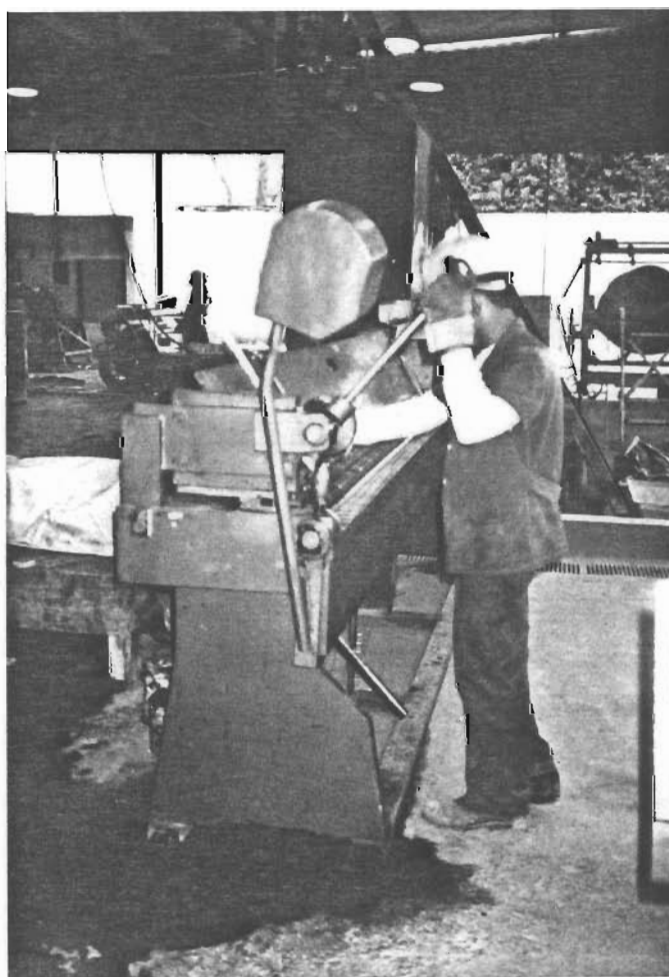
Mesas dobradeiras utilizadas no Cedec/Emurb.
